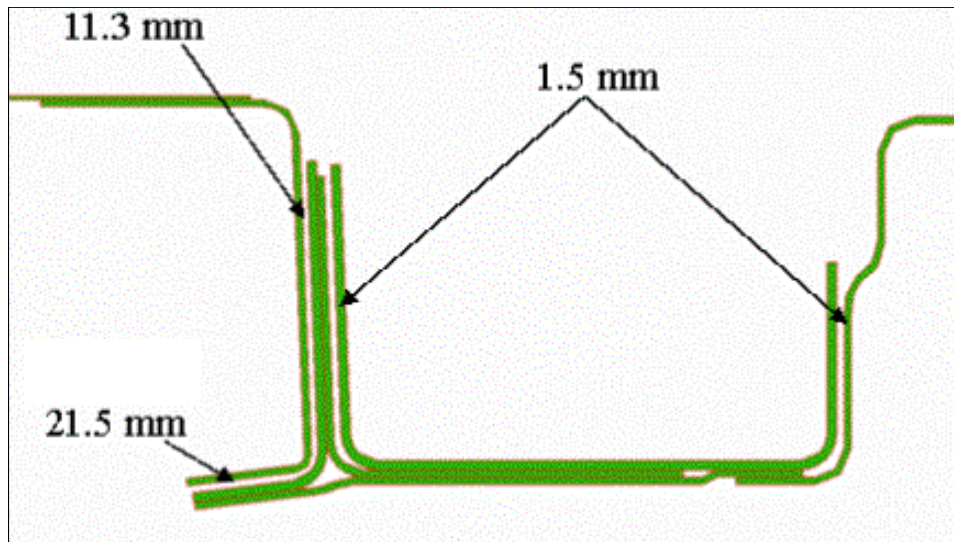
Exemplo de aplicação prática de espaçamento técnico
